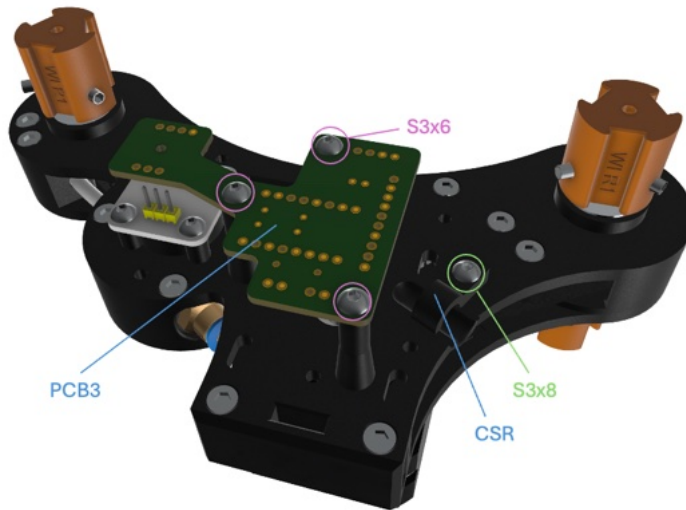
Rewinder-Chassis Montageschritt 26.
